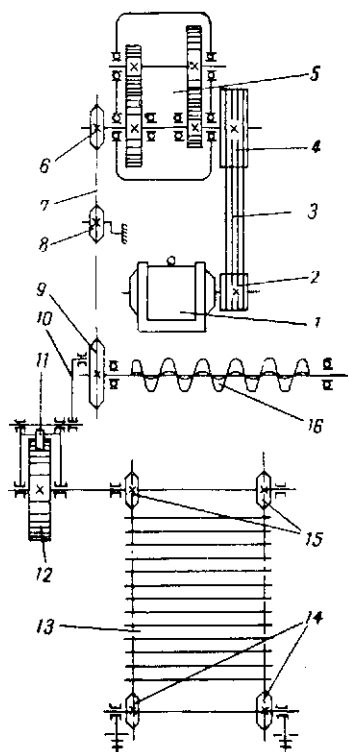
Кинематическая схема привода бункера-дозатора раздатчика РКС-3000:
